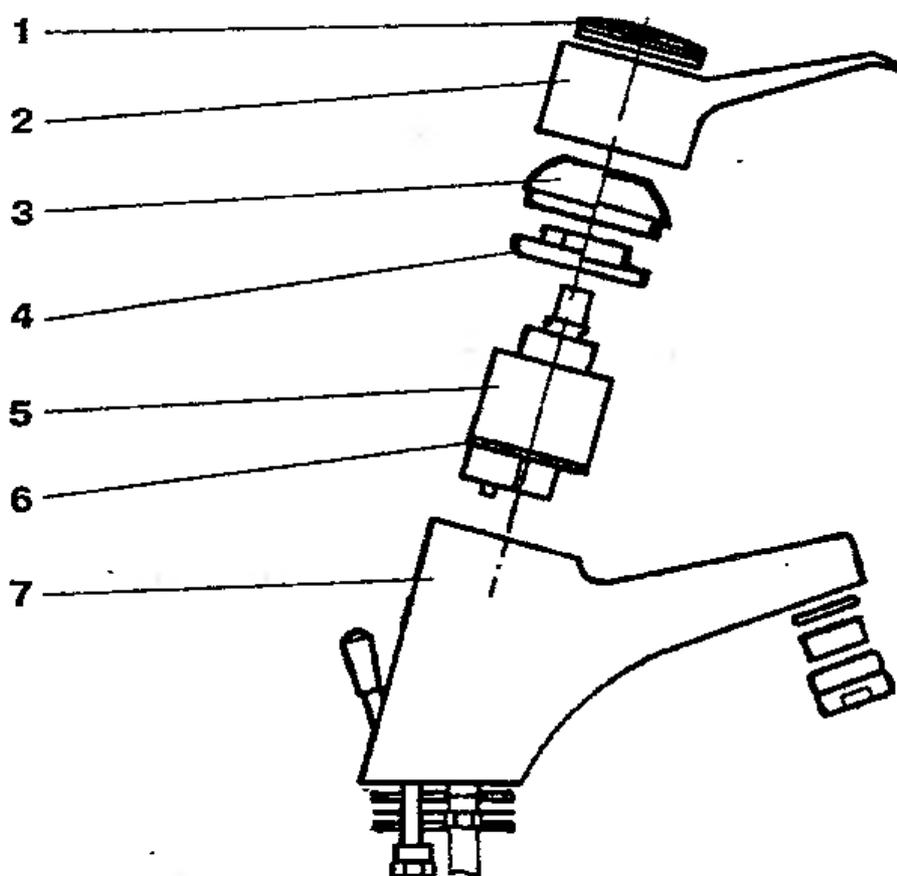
Устройство шарнирного смесителя с аэратором и встроенным фильтром: 1 — фиксирующий элемент; 2 — поворотная рукоятка (джойстик); 3 — крышка корпуса; 4 — круговая гайка; 5 — сменный картридж механической очистки; 6 — прокладка; 7 — корпус
